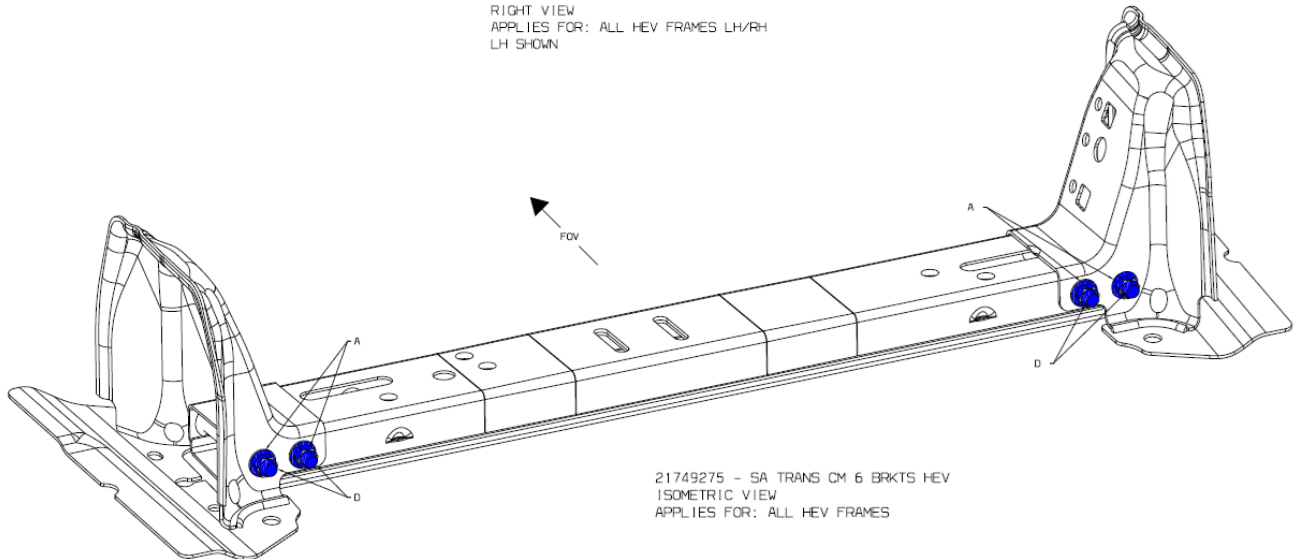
Sección 4, Información de Soldadura. [27]
